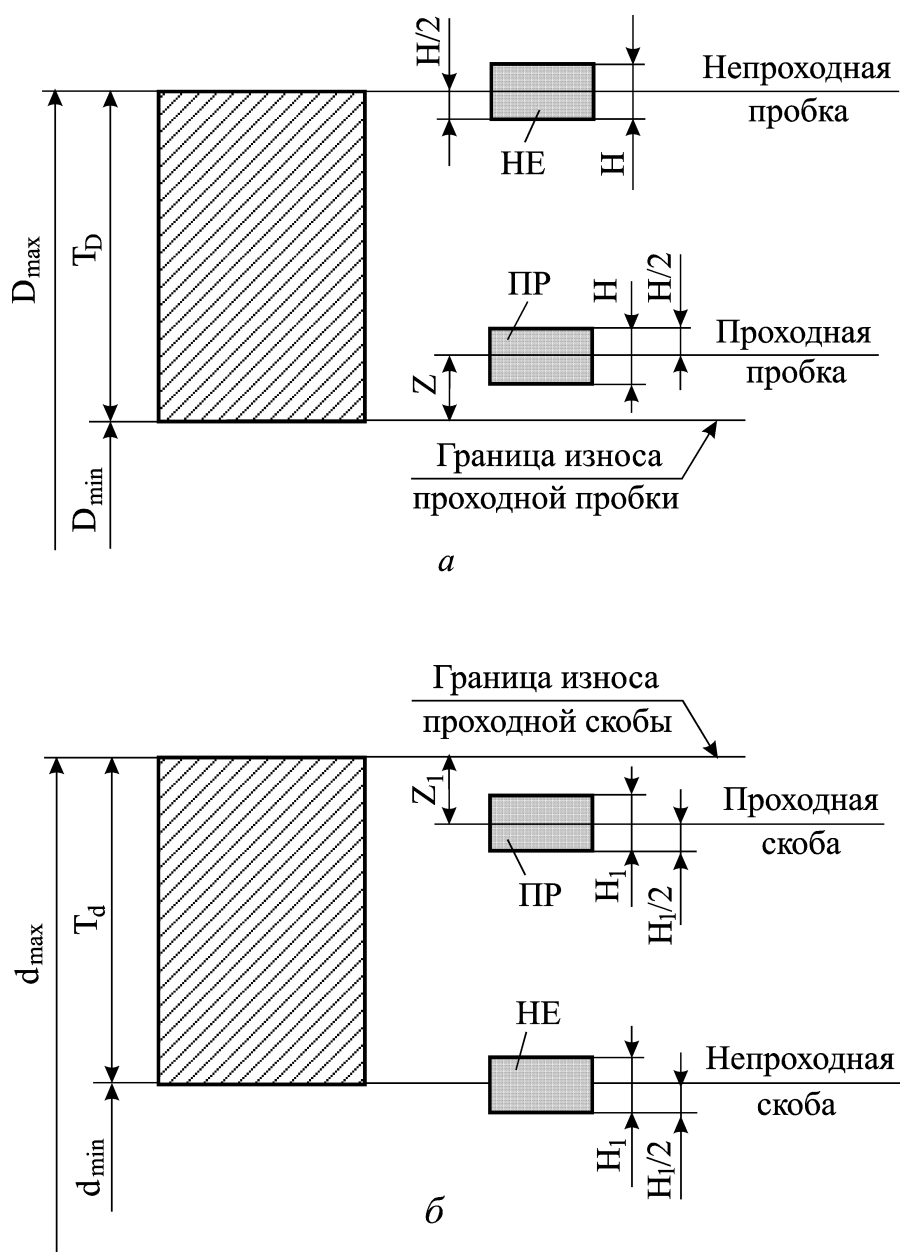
Схемы расположения полей допусков гладких калибров для контроля отверстий (а) и валов (б) с номинальными размерами до 180 мм и допуском изготовления по IT9-IT17
